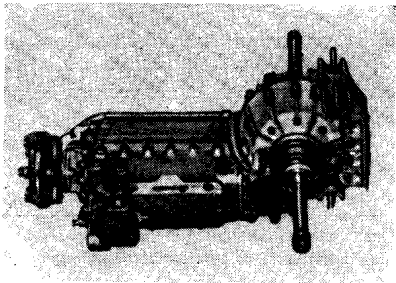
Образец моноблочной конструкции коробки передач и главной передачи
